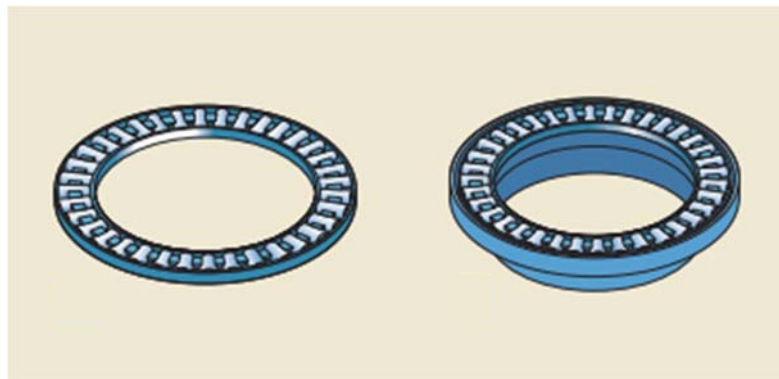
Rodamiento axial de rodillos cilíndricos
